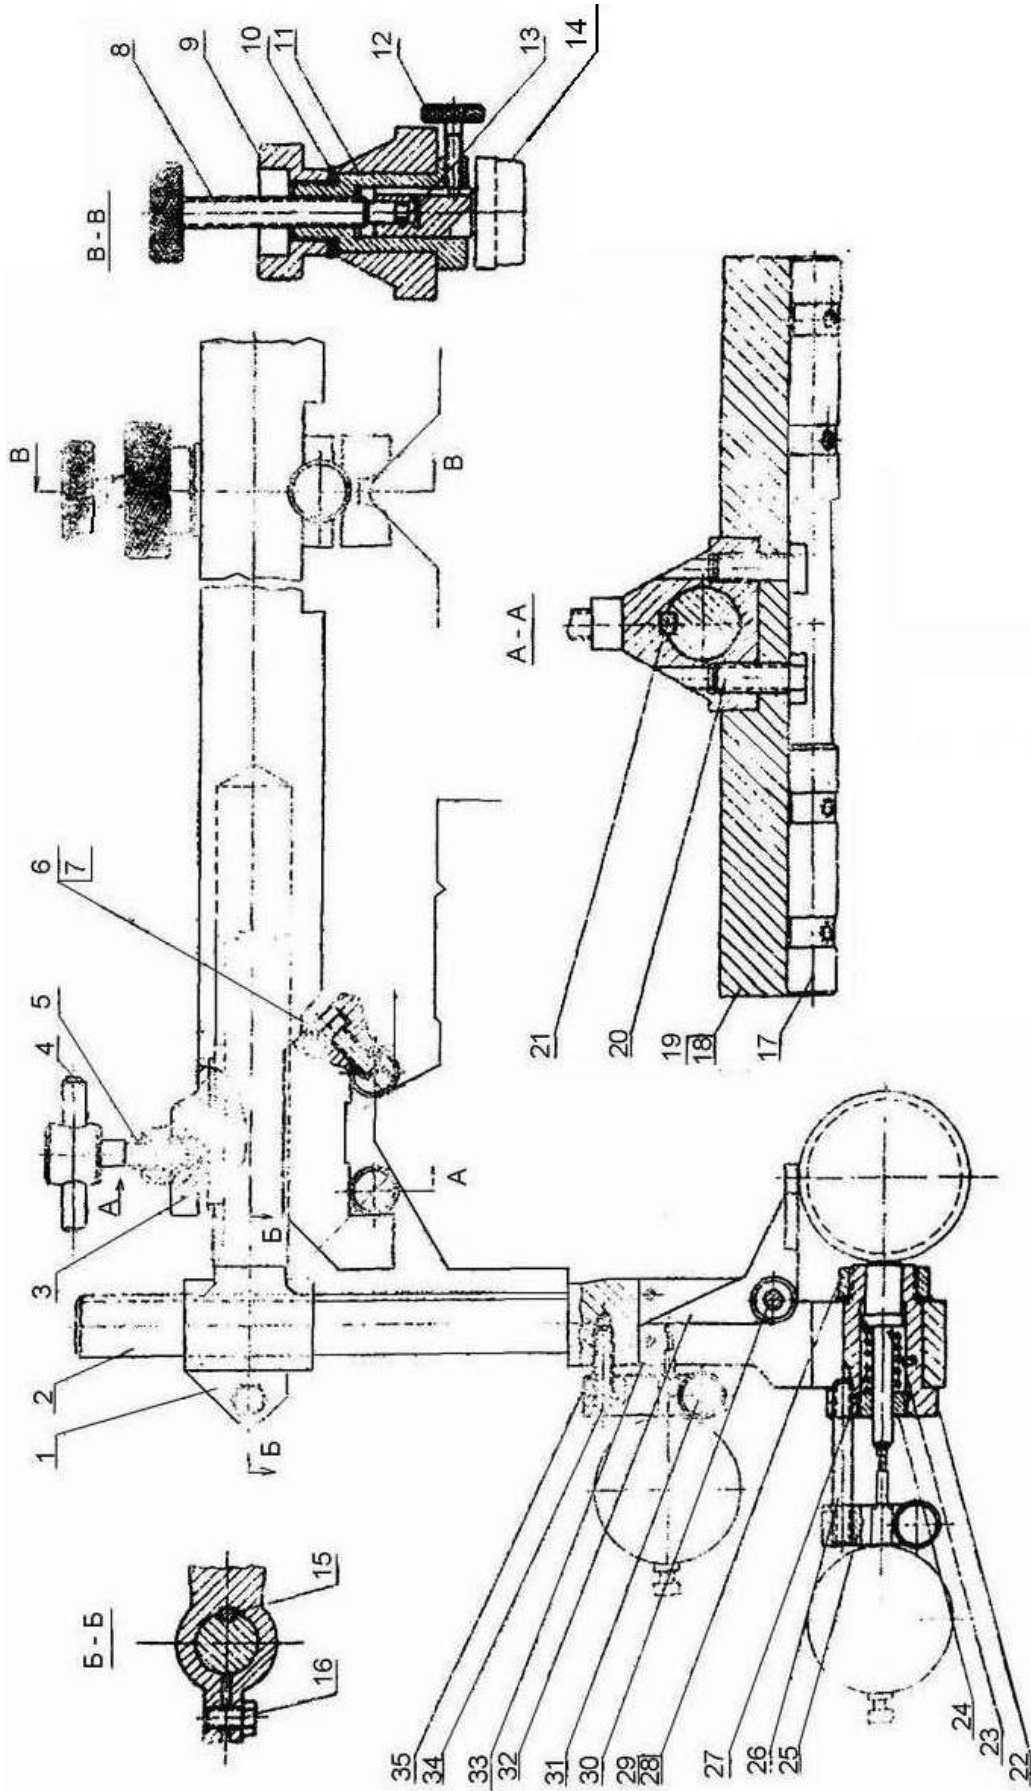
Приспособление для проверки ходовых винтов на токарных станках
